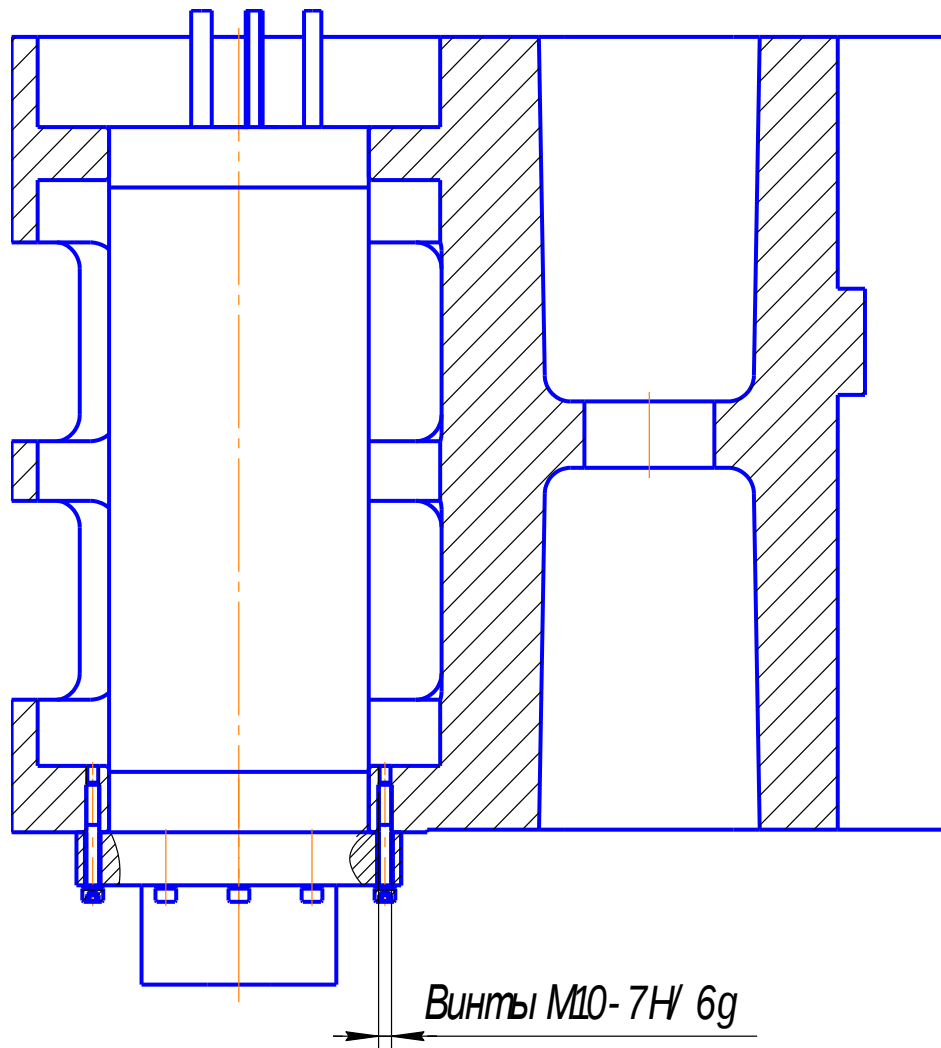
Конструкція корпусу шпиндельної головки
